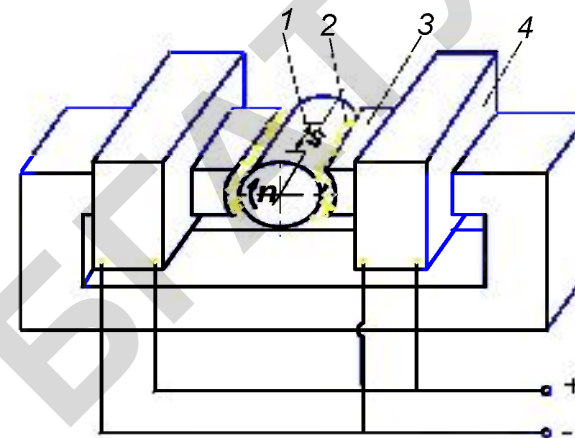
Схема магнитно-абразивной обработки: 1 – заготовка; 2 – ферромагнитный порошок; 3 – сердечник электромагнита; 4 – электромагнит
